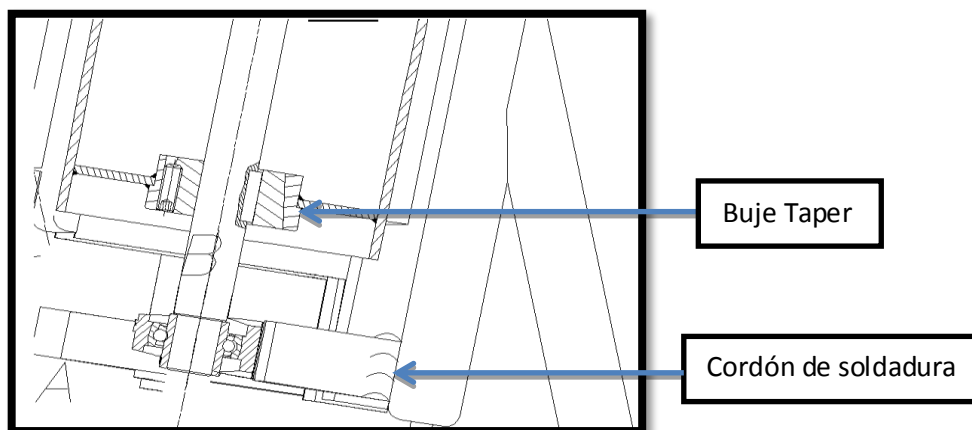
Muestra de soldadura en un extremo de eje
